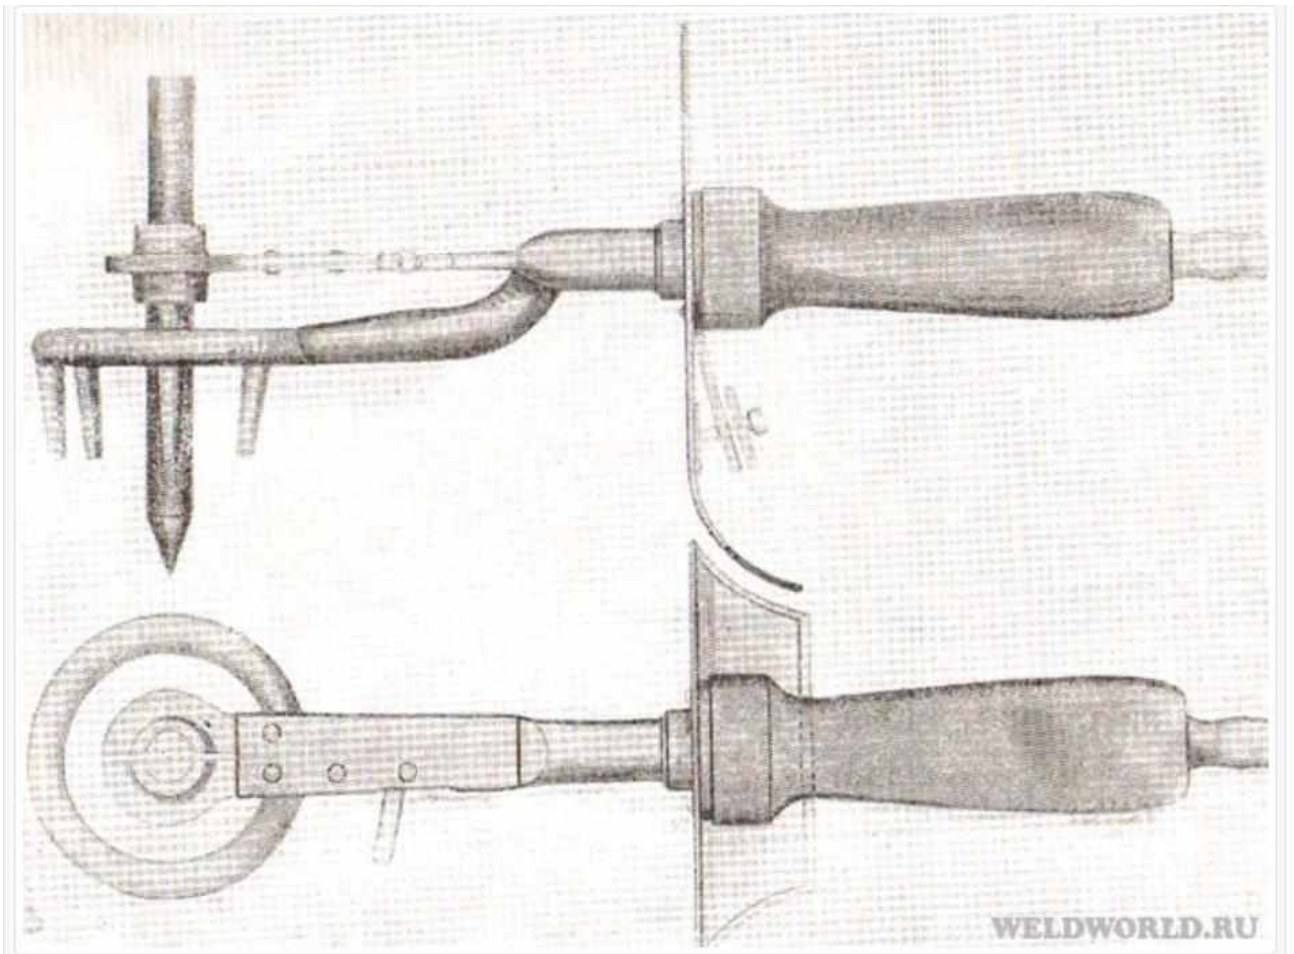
Suporte para soldagem a arco direto de carbono com gás de proteção – Weldworld.ru
